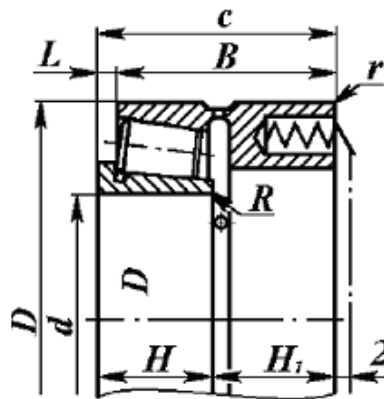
Однорядний роликовий конічний підшипник із широким зовнішнім кільцем типу 17000
